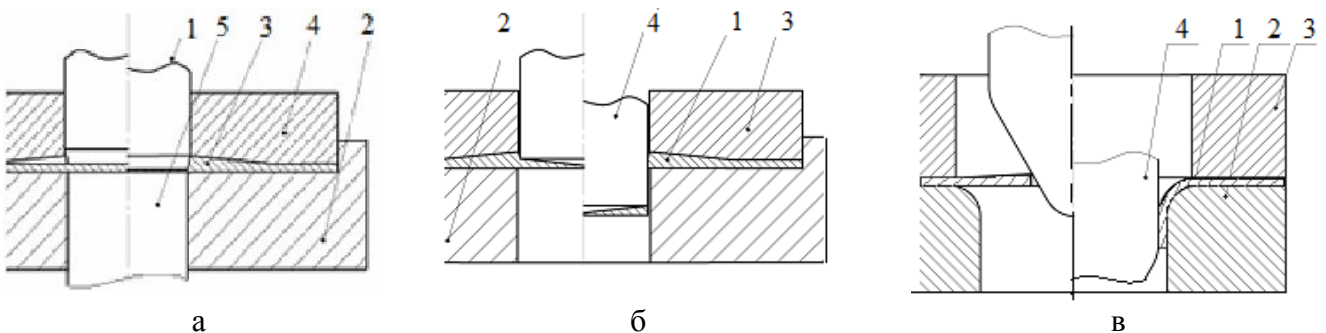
Попереднє профілювання видавлюванням (а), пробивання перемички (б) та відборткування заготовки (в): 1 – заготовка; 2 – матриця; 3 – притискач; 4 – пуансон; 5 – виштовхувач
